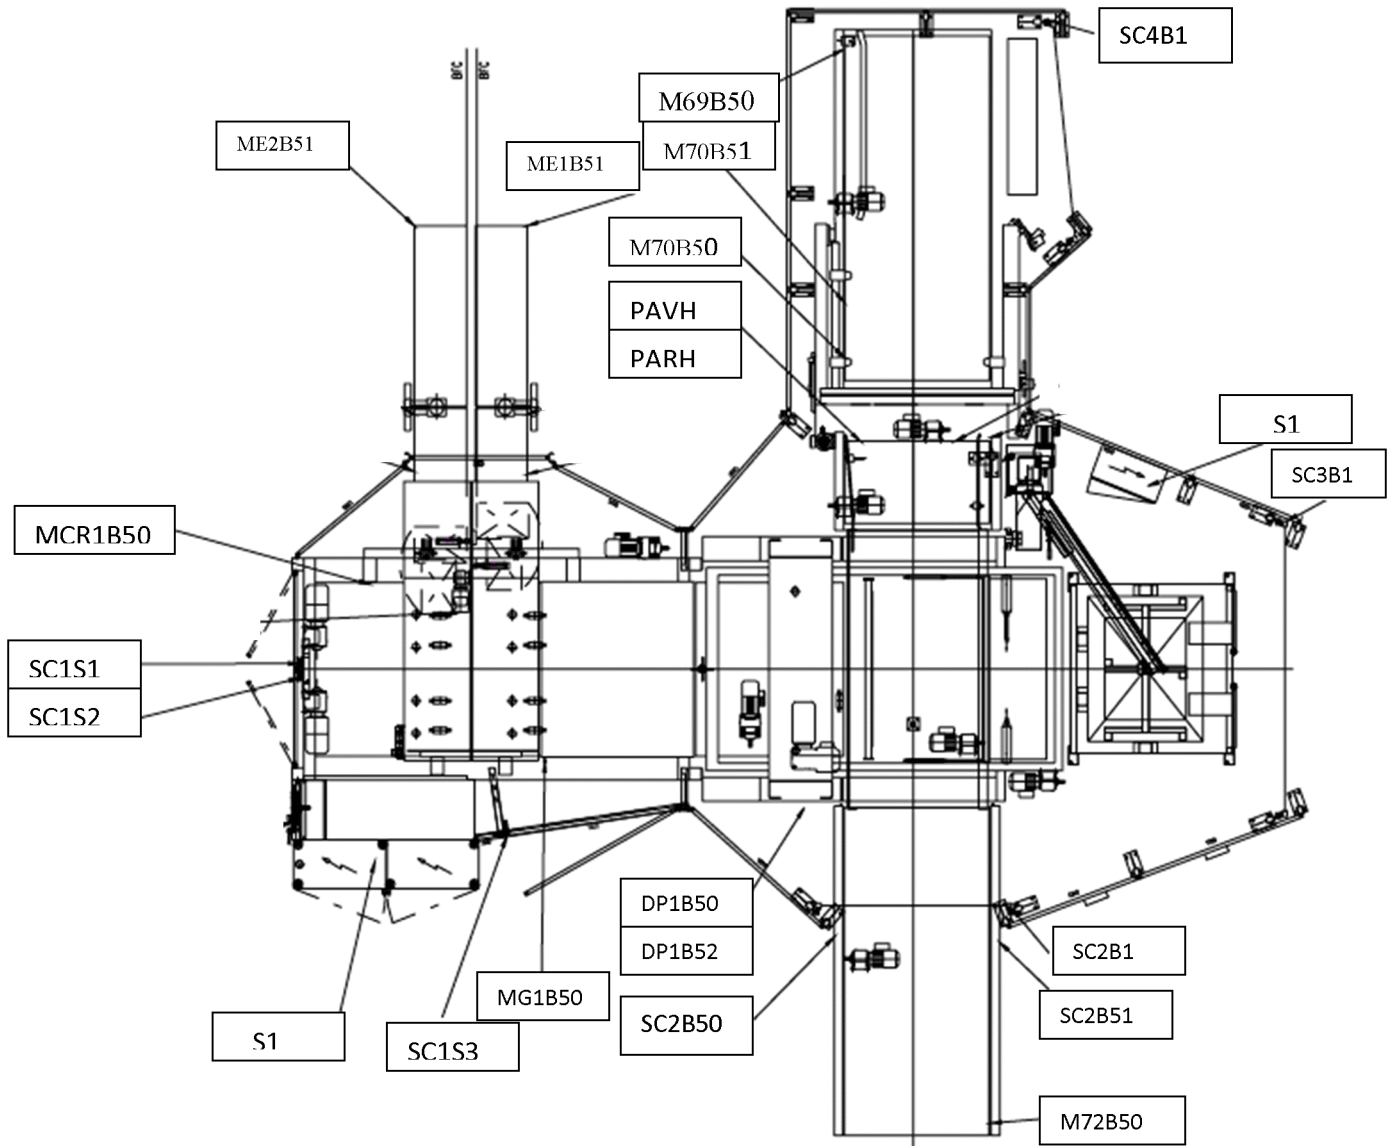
a : Implantation des capteurs vue du haut sur la machine palettiseur.
